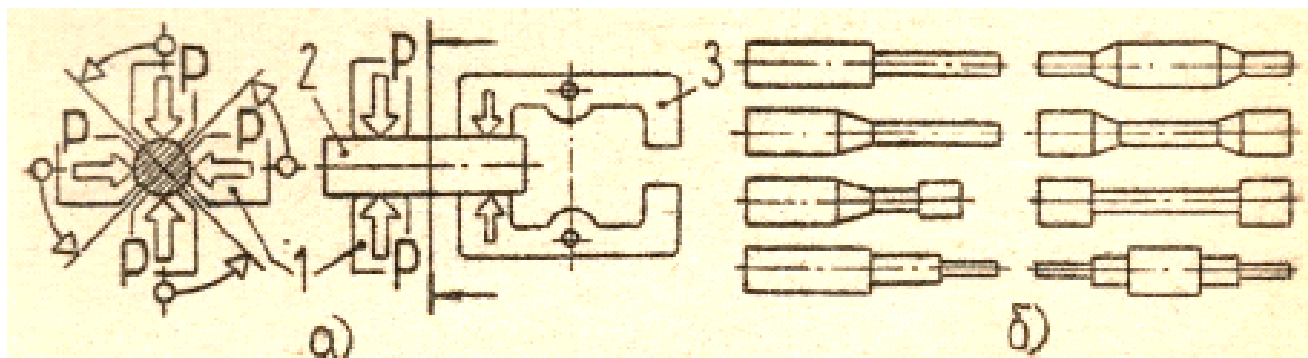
Схема профилирования на обжимной ковочной машине (а) и типовые поковки (б): 1 — бойки; 2 — обрабатываемая заготовка; 3 — клещевой захват
